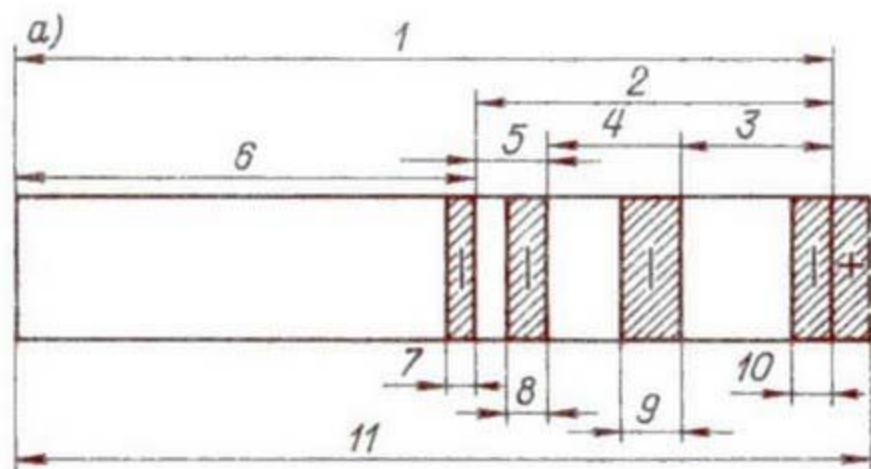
Основные сведения о размерной точности: а — допуски и припуски: 1 — номинальный размер заготовки; 2 — общий припуск; 3, 4 — припуск на черновую и чистовую обработку; 5 — припуск на шлифовку; 6 — наибольший предельный размер; 7 — допуск на шлифовку; б — микронеровности поверхности: 8, 9 — допуск на черновую и чистовую обработку; 10 и 11 — отрицательная и положительная часть допуска заготовки
